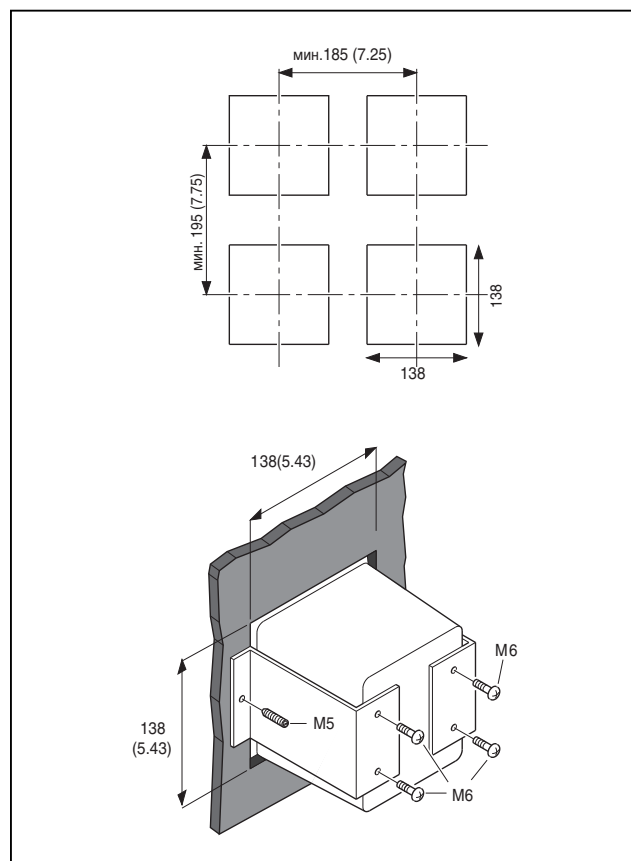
Опция /UM. Универсальный набор для монтажа, схема монтажа на панель
